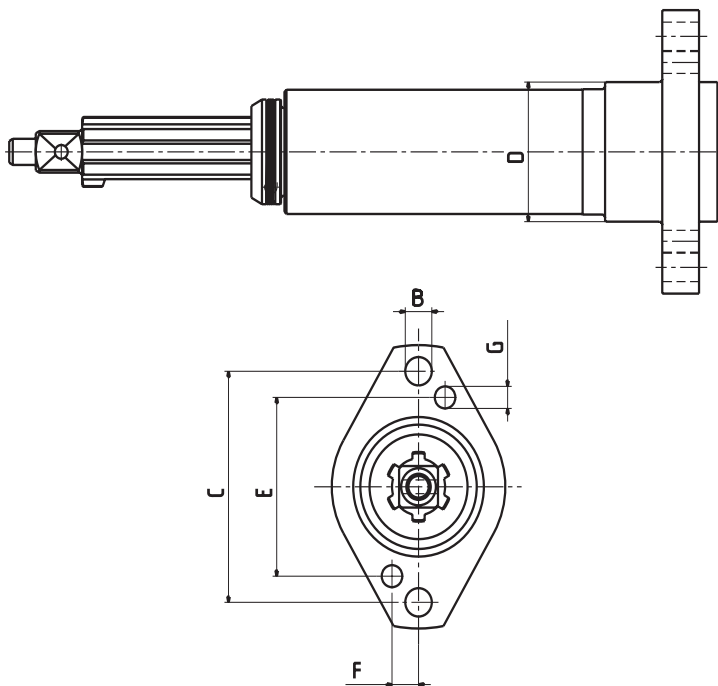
Hauptmaße zum Einbau auf einer Montageplatte (Geradabtrieb)
